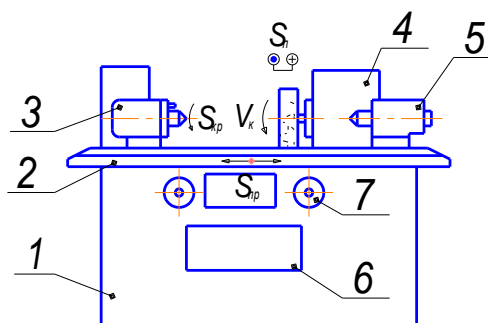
Общий вид круглошлифовального станка 3Б12
